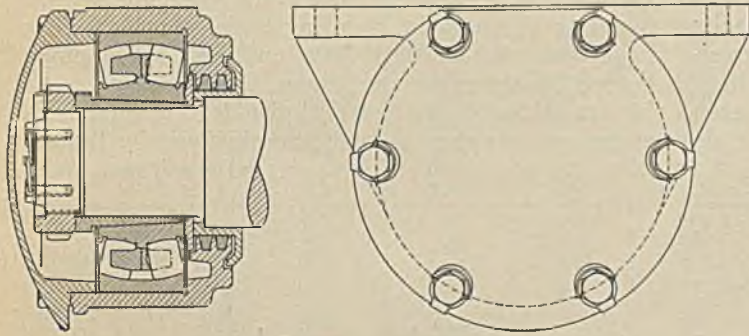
Pendelrollenlager der Vereinigten Kugellagerfabriken-A. G. in Schweinfurt für Außenlagerung von Förderwagenachsen.
